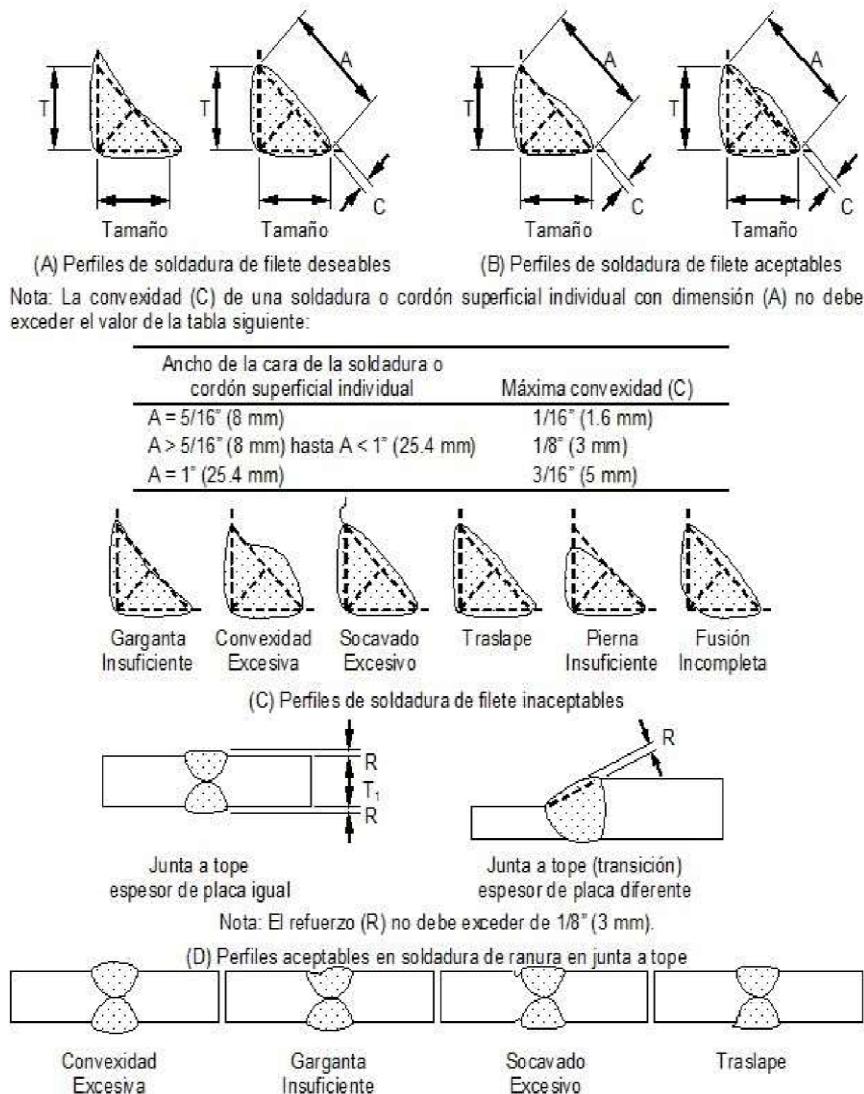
Perfiles inaceptables en soldadura de ranura en junta a tope.
